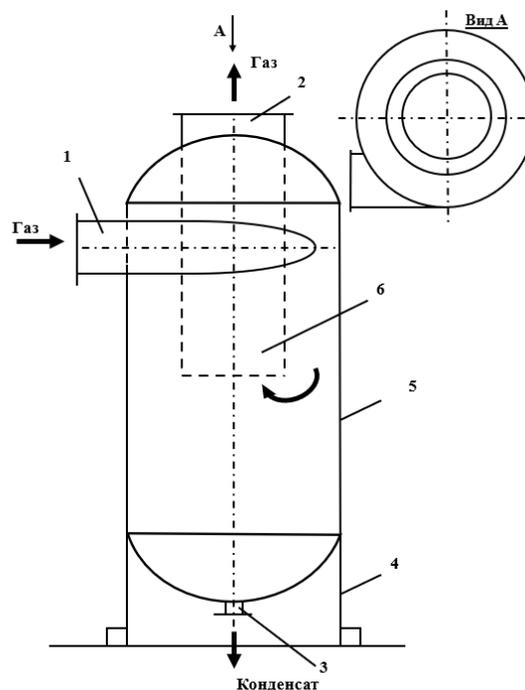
Реконструкция газового сепаратора: 1 – входной штуцер для газа (тангенциальный подвод); 2 – выходной штуцер для газа; 3 – штуцер для выхода конденсата; 4 – опора аппарата; 5 – корпус аппарата; 6 – соосная труба.
